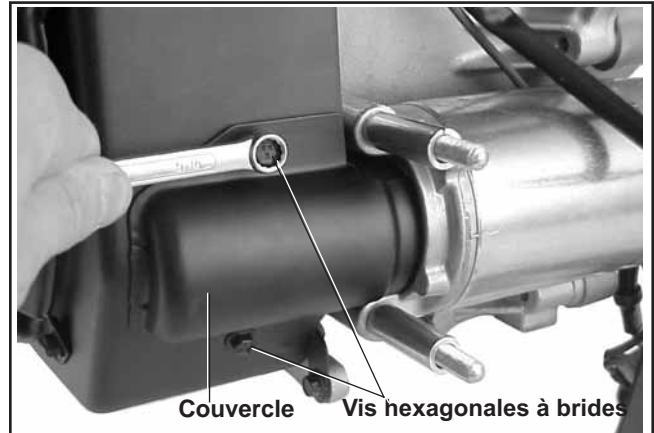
Retrait du couvercle du démarreur (pignon).
